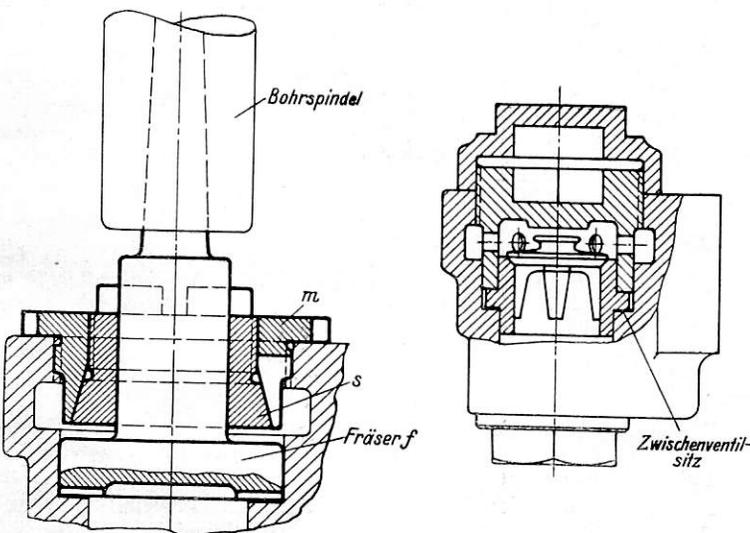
Fräser für Luftpumpen-Instandsetzung.
